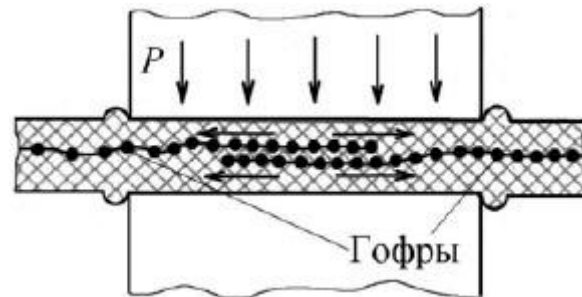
Схема течения полимерной матрицы в процессе сварки и образование гофр армировки в околошовной зоне
